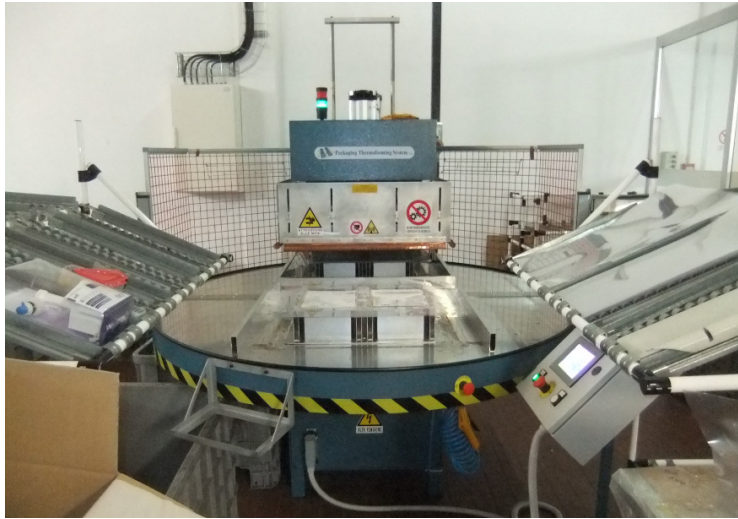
Equipamento de soldadura dos *blisters
